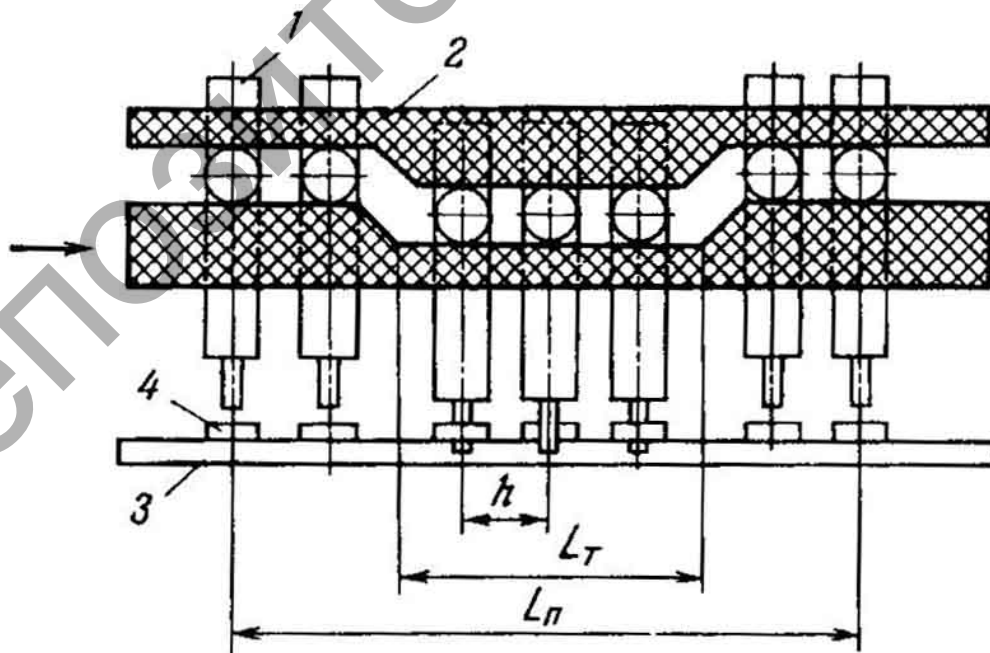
Схема роторного автомата (развертка барабана)
